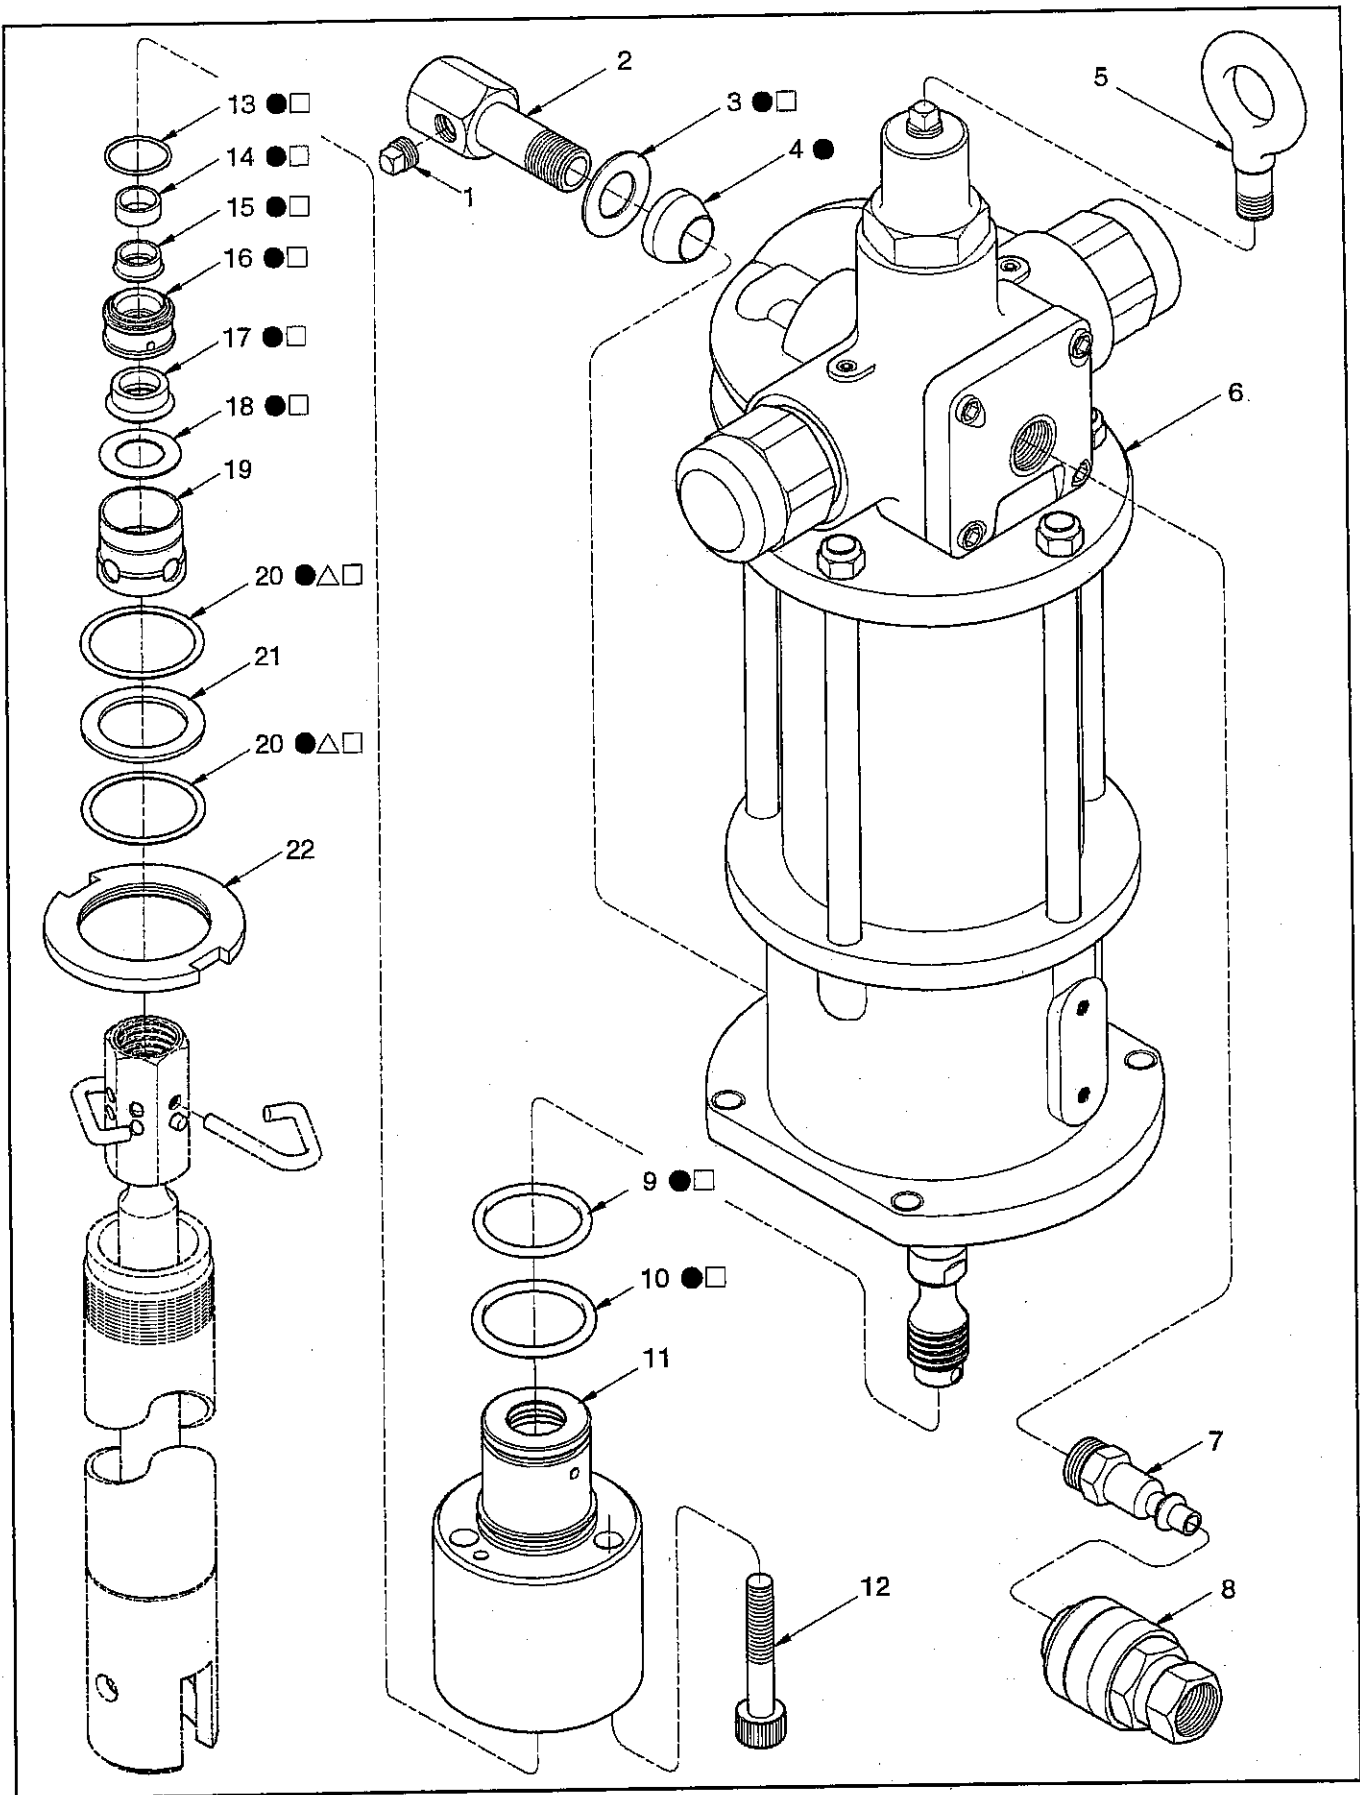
A Hochdruck-Schmierpumpe, Modellreihe 7785 - Explosionszeichnung
